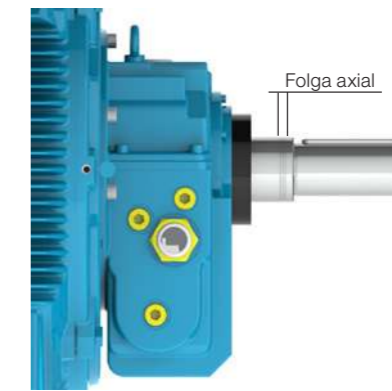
Folga axial em motor equipado com mancal de deslizamento.
